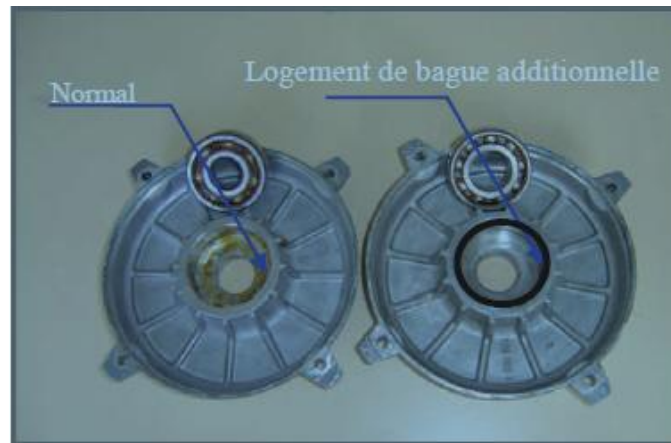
Vue d'un flasque de machine sans et avec bague additionnelle d'excentration [4].
